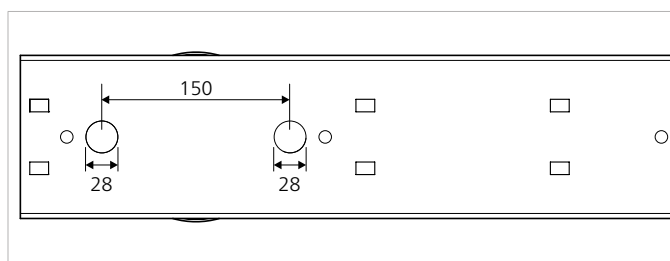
Abmessungen Löcher Ein-/Auslassrohr (Angaben in mm)
